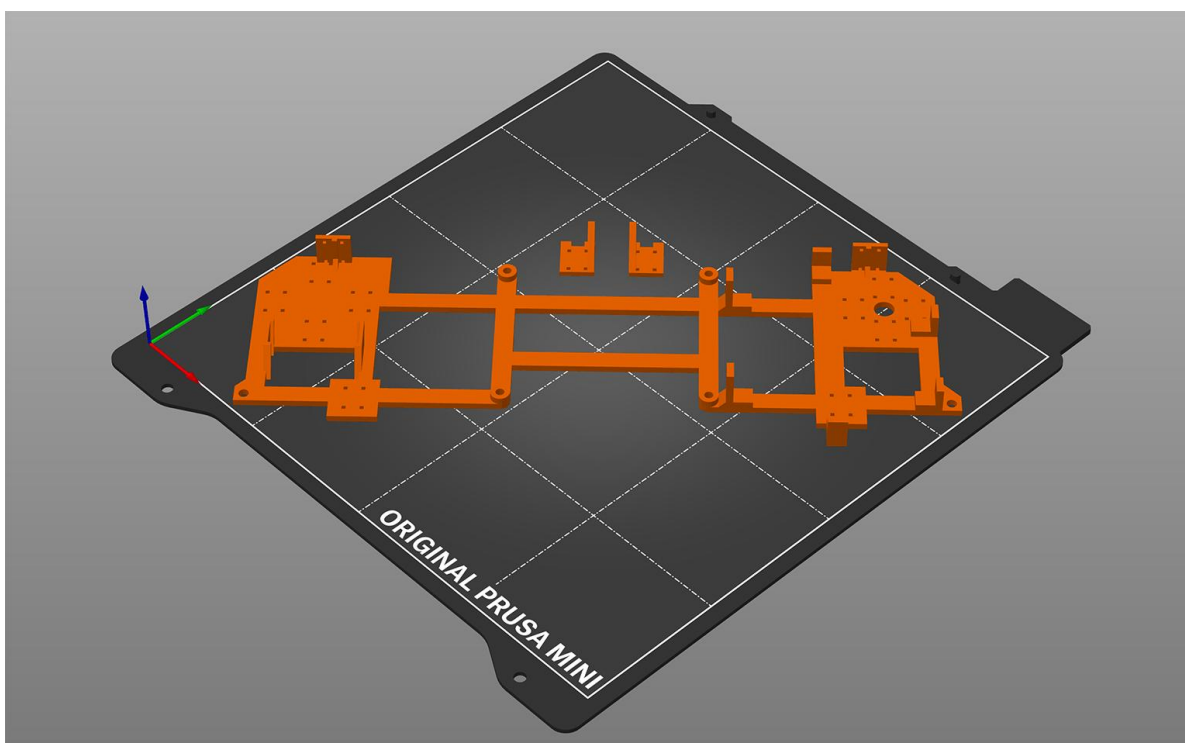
Файл pcb-prototype-v0.stl
